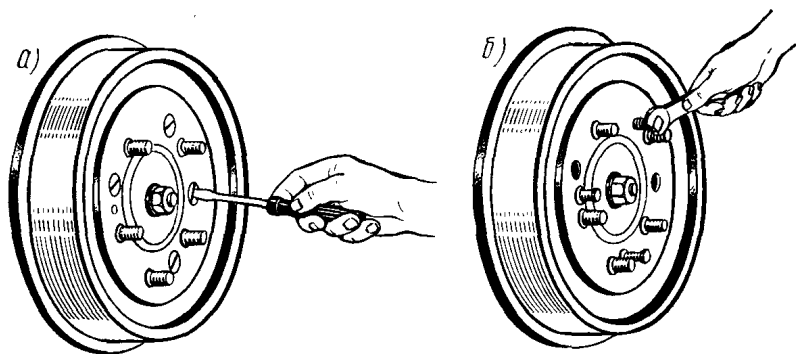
Снятие тормозного барабана со ступицы колеса:
